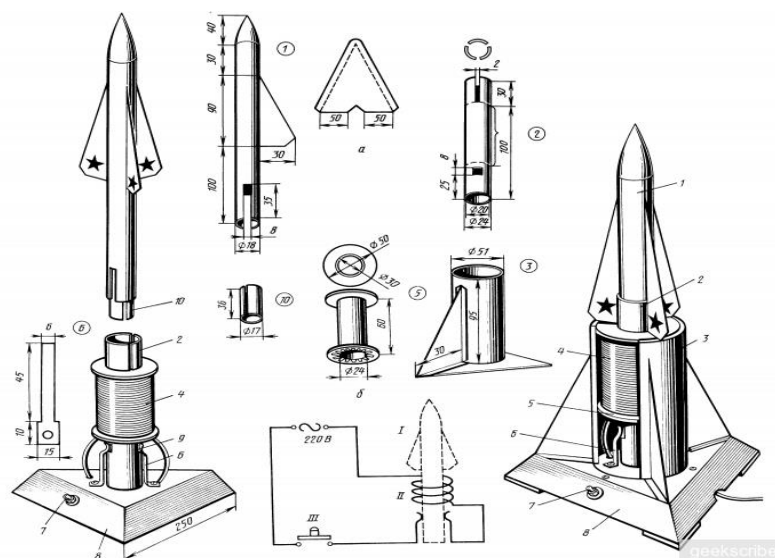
Пусковая установка «Малыш»: 1 — модель ракеты; 2 — направляющая трубка; 3 — корпус; 4 — обмотка; 5 — каркас катушки; 6 — контакты; 7 — кнопка пуска; 8 — основание; 9 — окно для контактов; 10 — сердечник; а — развертка стабилизатора; б — электрическая схема; I — модель; II — катушка; III — пусковая кнопка; IV — контакты
